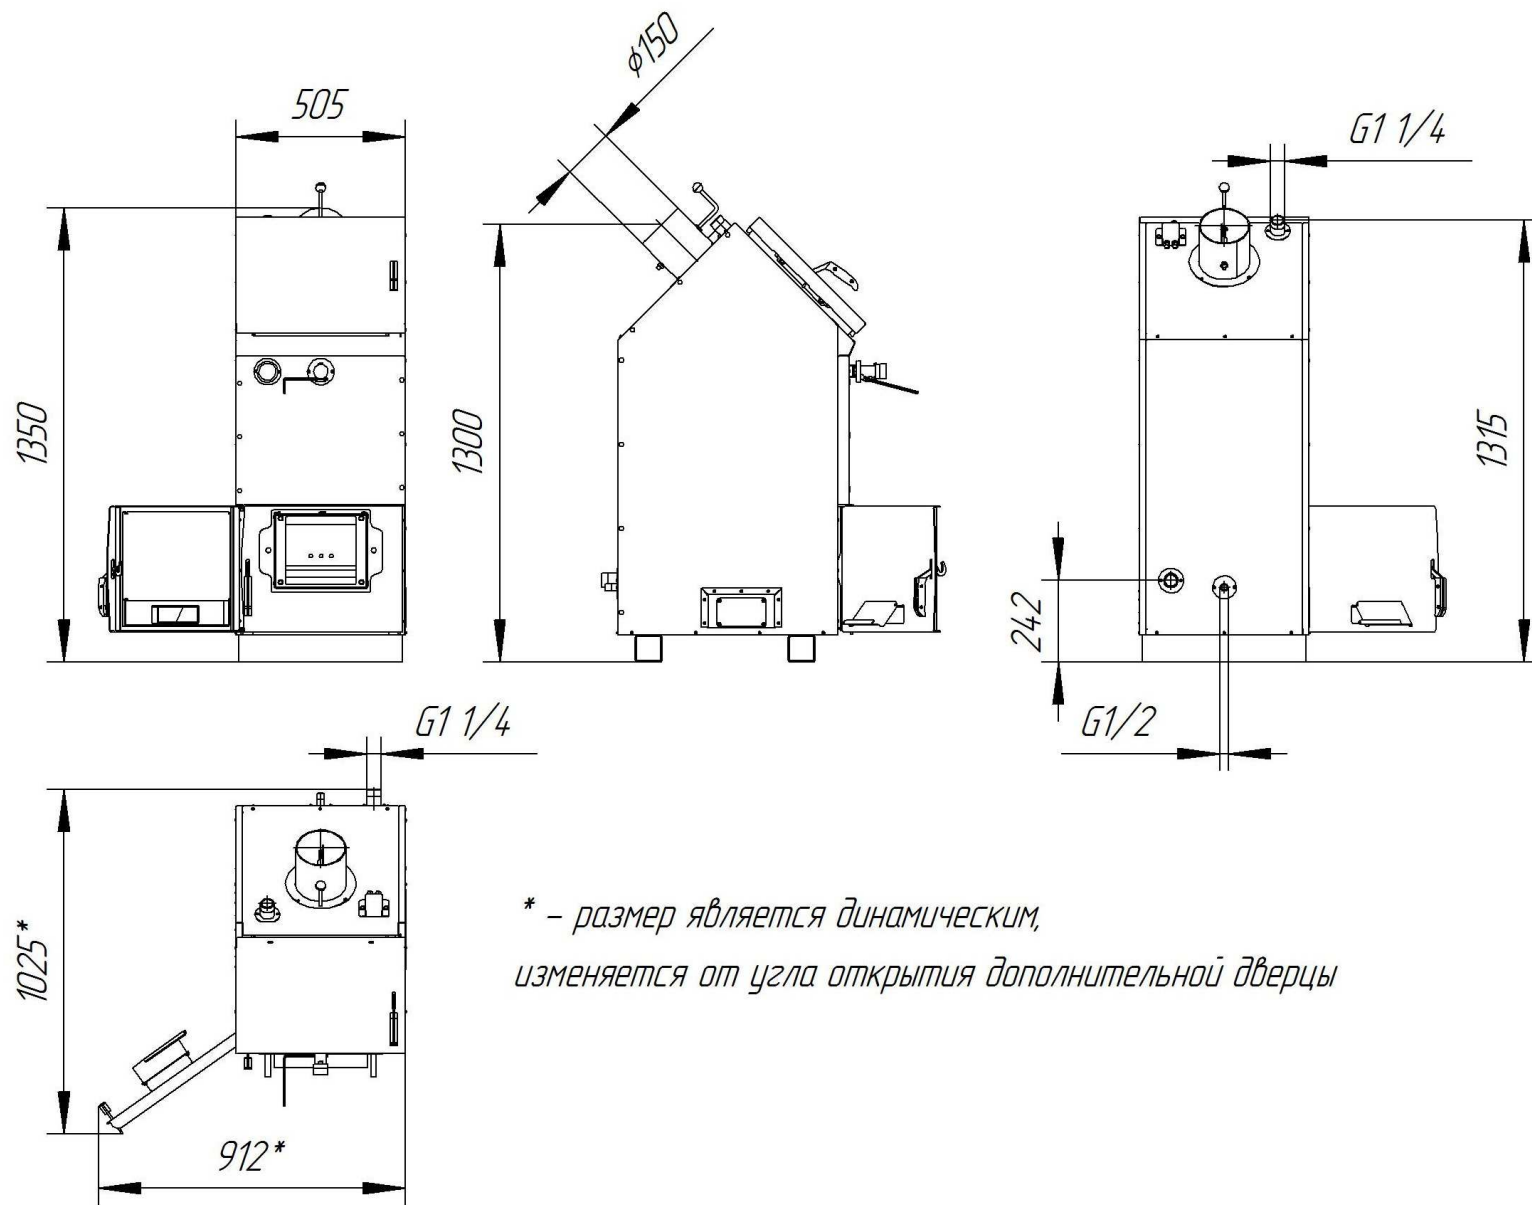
Габаритные и присоединительные размеры котла Bioten GX-25.
